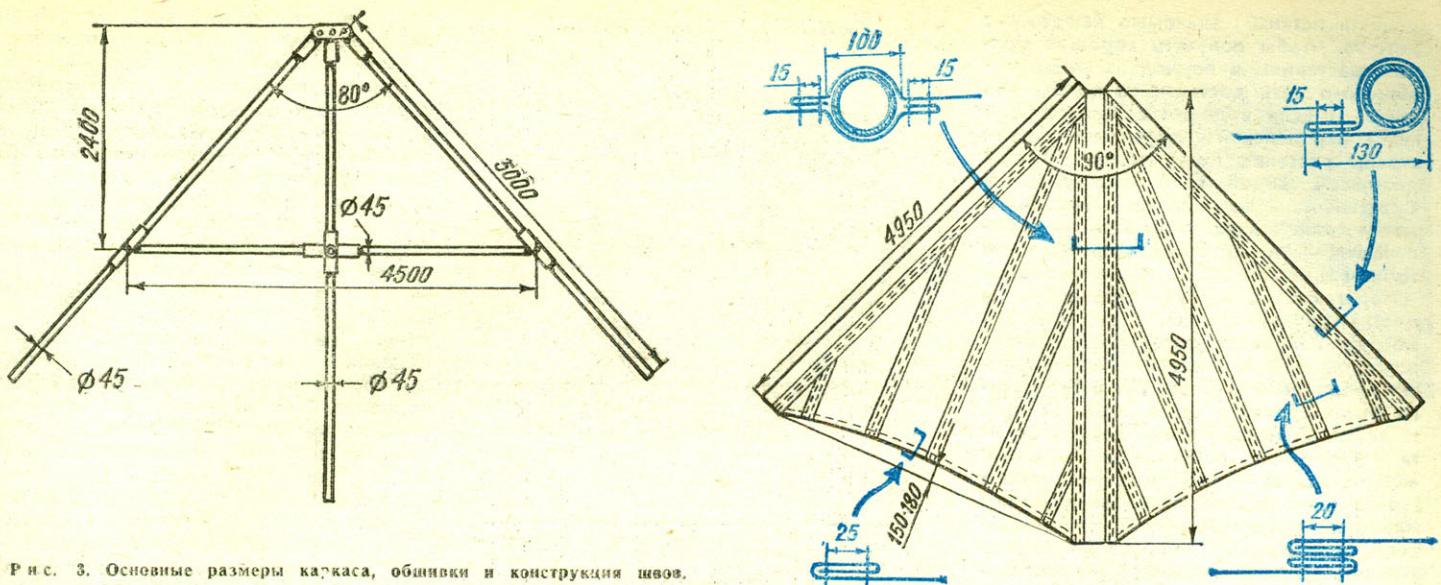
Основные размеры каркаса, обшивки и конструкция швов.
